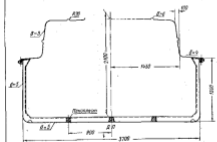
Примерный конструктивный шаблон-диаметр буксирного катера мощностью 90 л. с. с пластмассовым корпусом.
